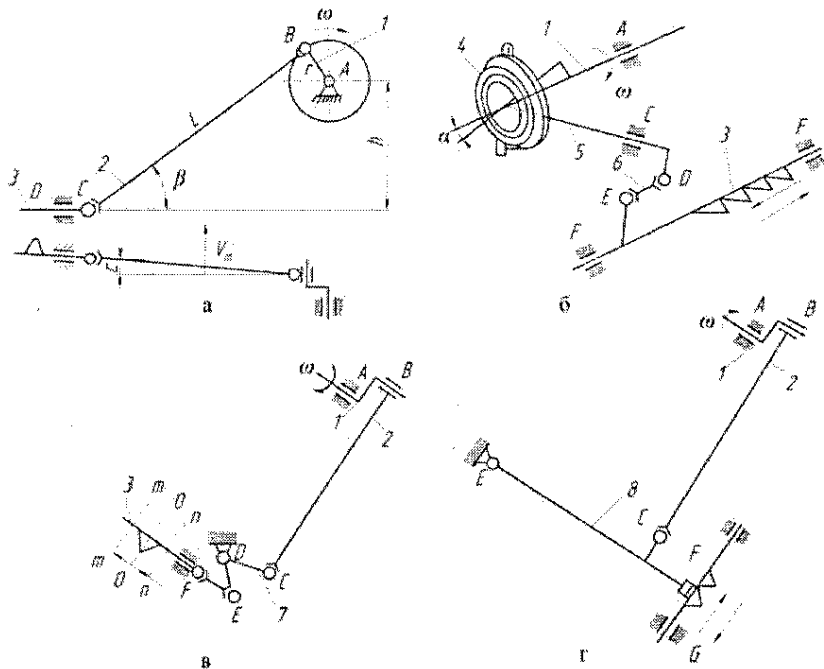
Схеми механізмів приводу ножа: а – кривошипно-повзунний; б – коливальної шайби; в – кривошипно-повзунний з коромислом; г – кривошипно-повзунний з водилом; 1 – кривошип; 2 – шатун; 3 – ніж; 4 – коливальна шайба; 5 – вилка; 6 – з'єднувальна ланка; 7 – коромисло; 8 – водило.
